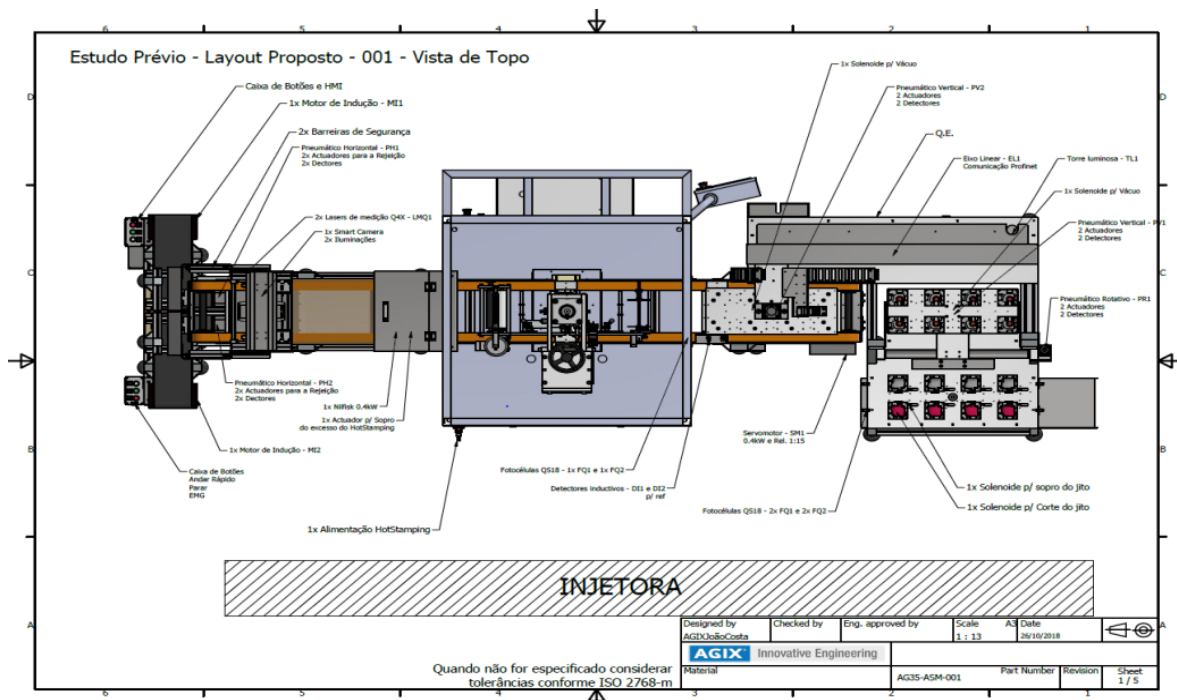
AG35-ROCKER - Layout de equipamentos a eletrificar
